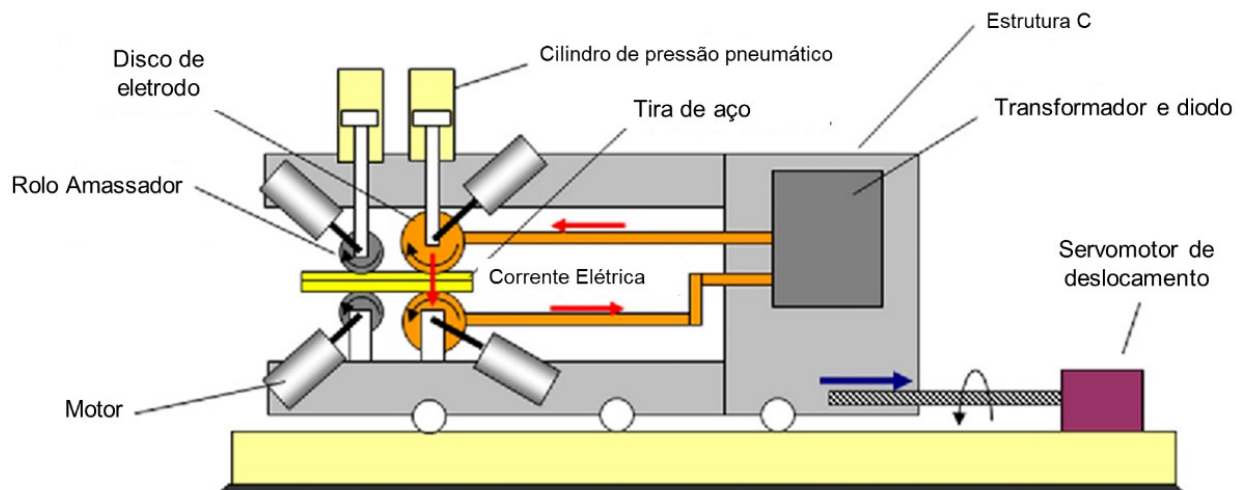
Figura esquemática do equipamento de soldagem por costura.
